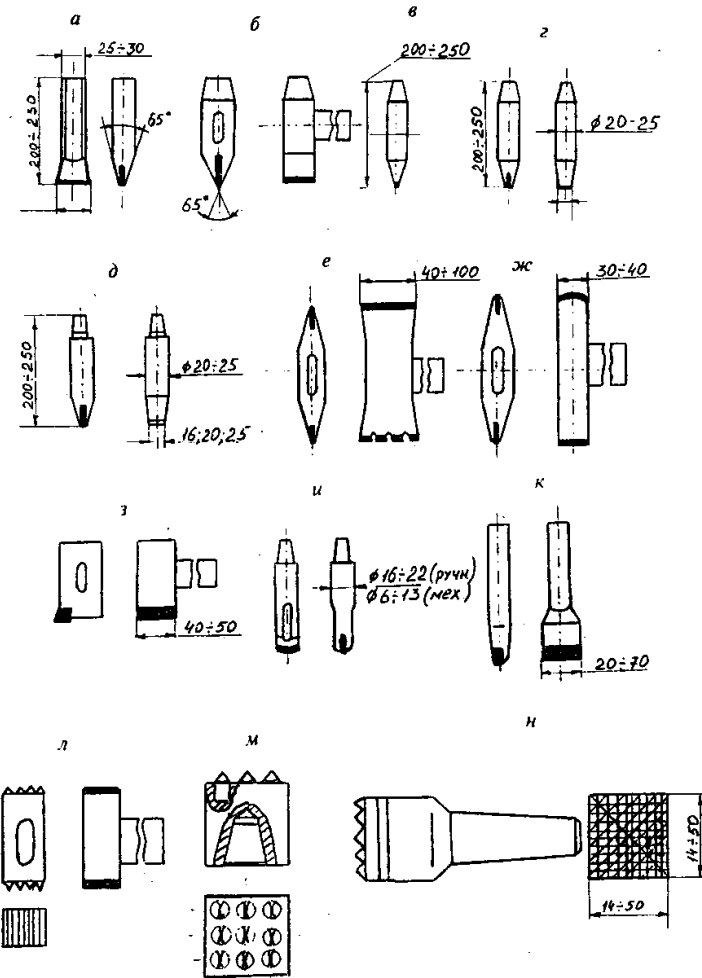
Инструмент из твердого сплава для обработки камня скалыванием: а, б — закольники; в — шпунт; г — ручная скарпель; д — механическая скарпель; е — топорик двухсторонний; ж — кайло двухстороннее; з — киянка (молоток); и — долото (бур) ручное или механическое; к — отбойник; л — бучарда механическая насадная; н — бучарда механическая с хвостовиком
